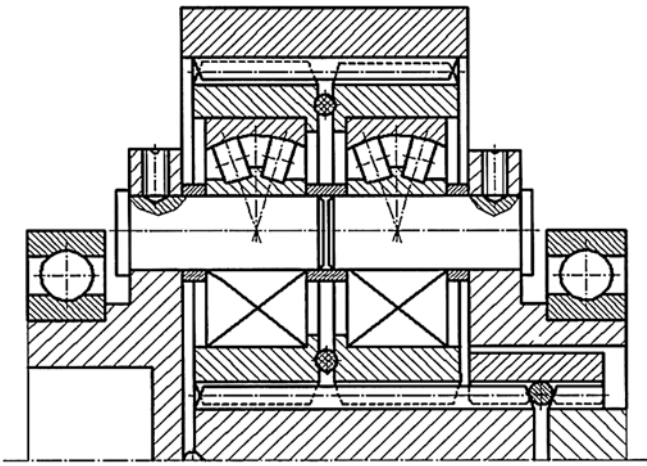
Планетарная передача с двухрядными сателлитами и самоустанавливающейся центральной шестерней
